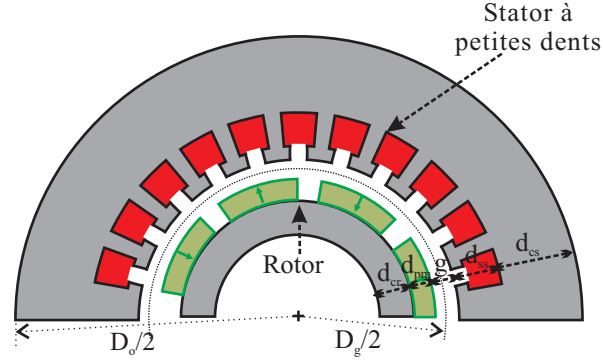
Les principales dimensions de la machine à flux radial
